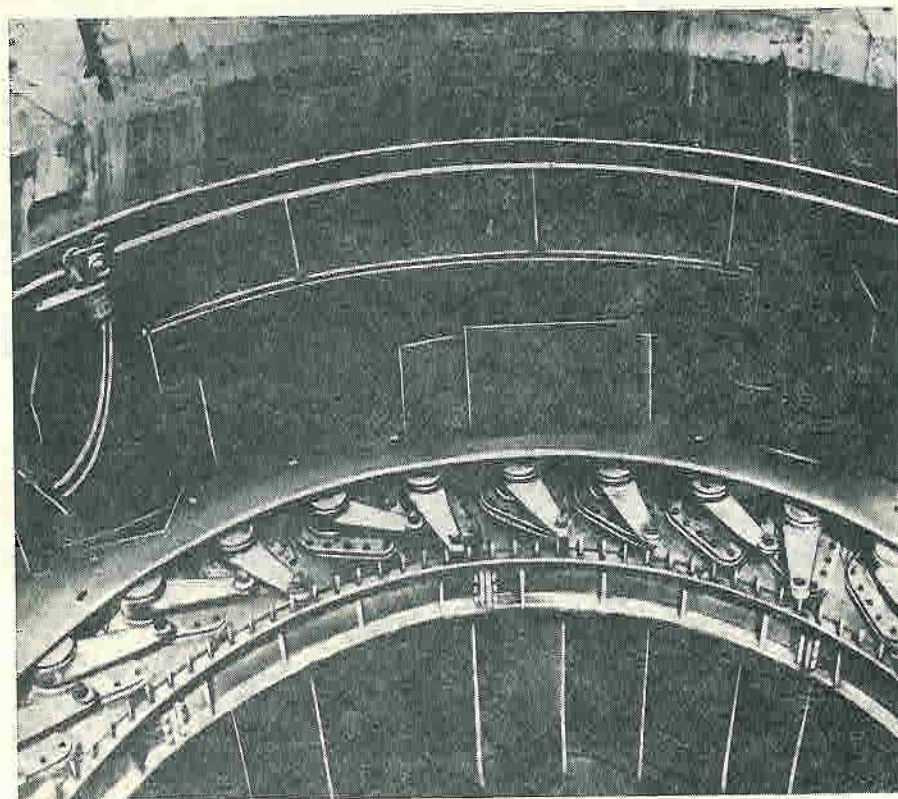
Общий вид сборки направляющего аппарата с установкой рычагов до опускания рабочего колеса
